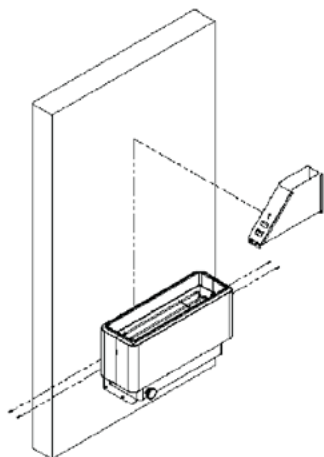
Установка цоколя дымохода на устройство и крепление винтами
